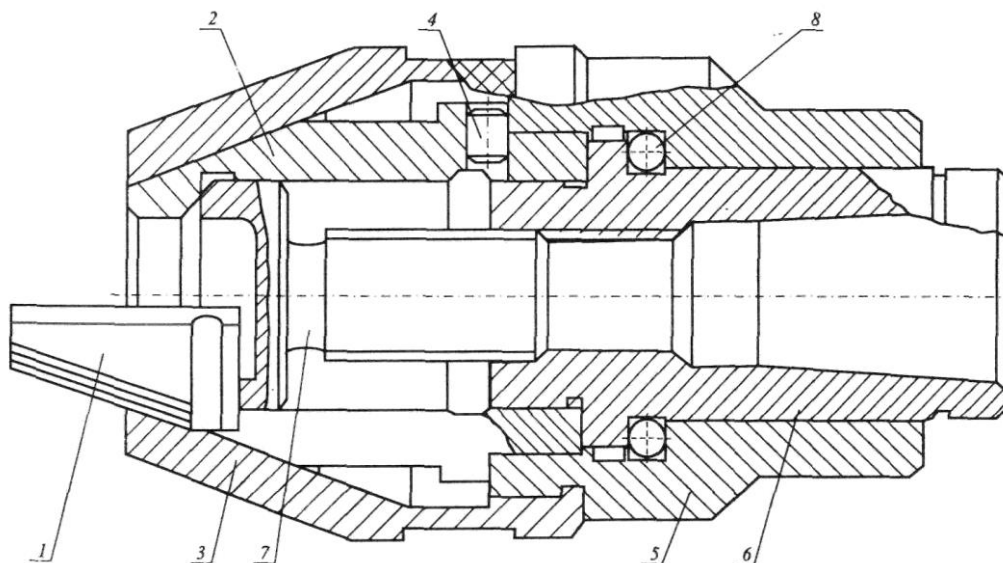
Патрон свердлильний безключевий: 1 – кулачки (3); 2 – обойма; 3 – гайка; 4 – штифт; 5 – втулка; 6 – корпус; 7 – головка з лівою різьбою; 8 – кульки
